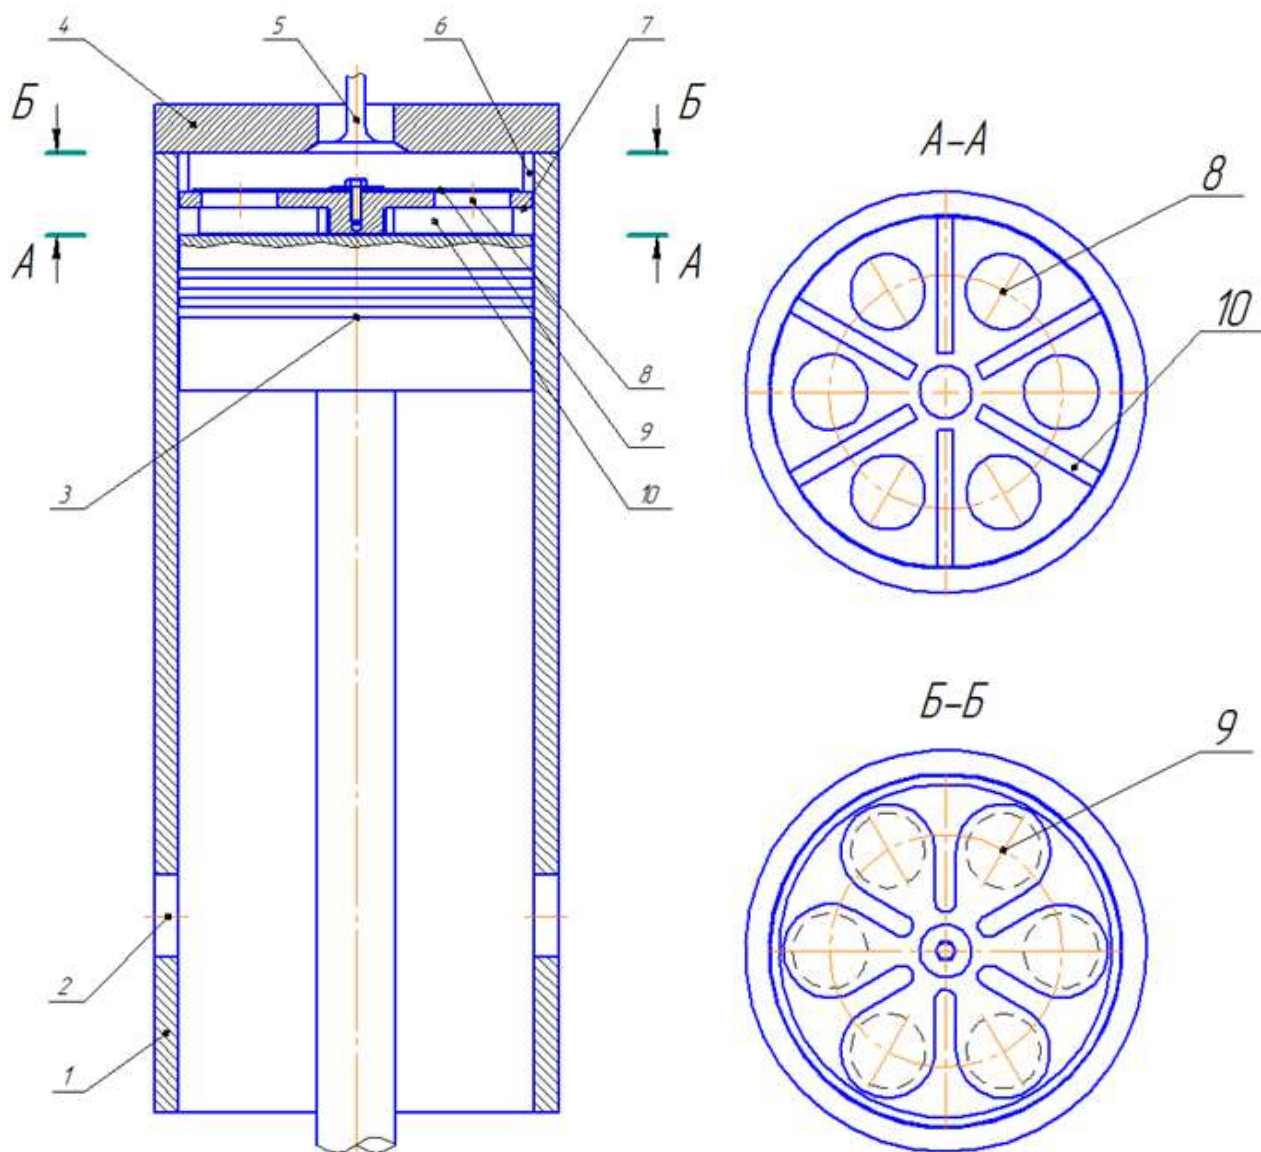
Положення поршня і газового поршня у верхній мертвій точці: 1 – циліндрова втулка; 2 – продувні вікна; 3 – поршень; 4 – кришкою циліндра; 5 – випускний клапан; 6 – дистанційне кільце; 7 – газовий поршень; 8 – повітряні отвори; 9 – клапани; 10 – ребра жорсткості
